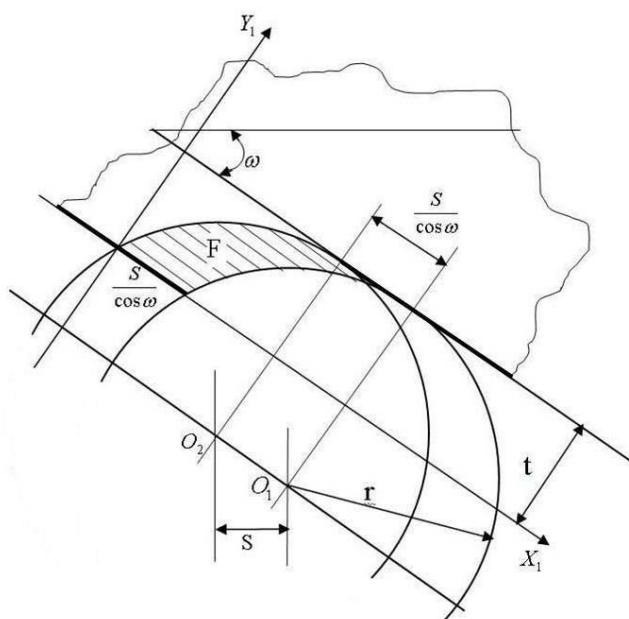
Схема снятия припуска резцом с круглой режущей пластиной на конической части заготовки при входе резца во впадину профиля
